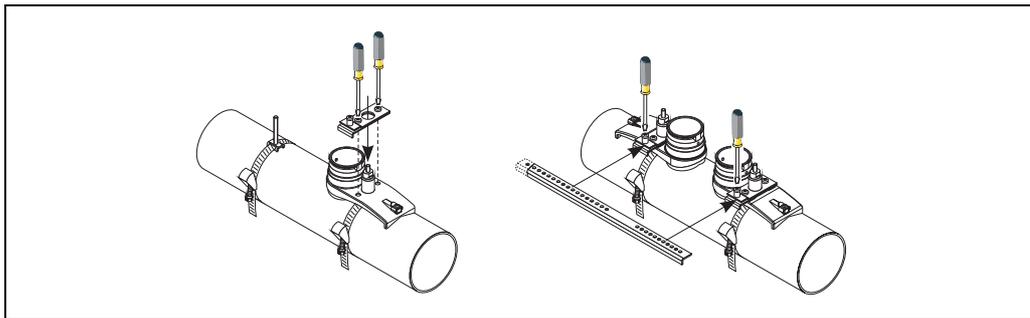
Montaggio dei supporti per sensori e della guida di posizionamento
